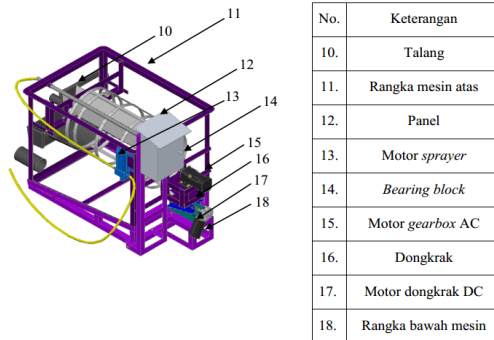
3 Mesin *Rotary Drum Filter 3M
